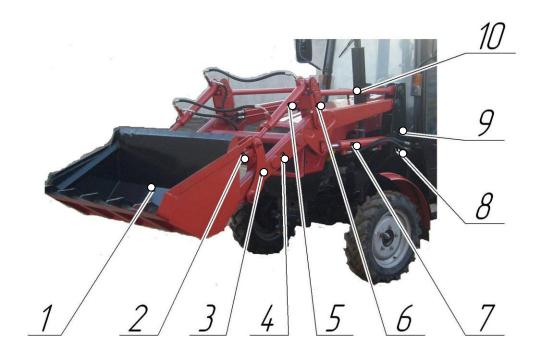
Общий вид оборудования погрузочного. 1 - Сменное навесное оборудования (Ковш), 2 - Тяга, 3 - Рычаг, 4 - Стрела, 5 - Гидроцилиндр ковшевой, 6 - Маятник, 7 - Гидроцилиндр стреловой, 8 - Стойка, 9 - Штанга распорная, 10 - Стабилизатор.
